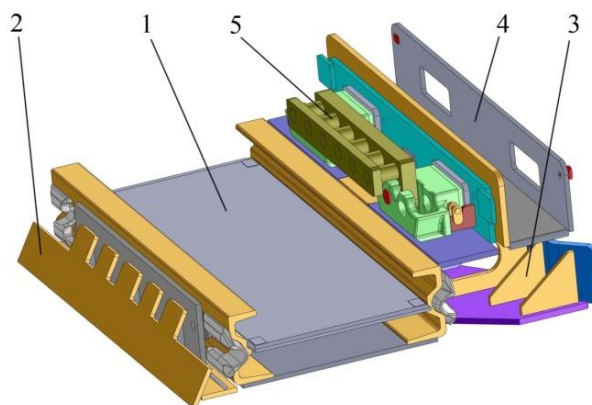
Рештак забойного скребкового конвейера с навесным оборудованием:
